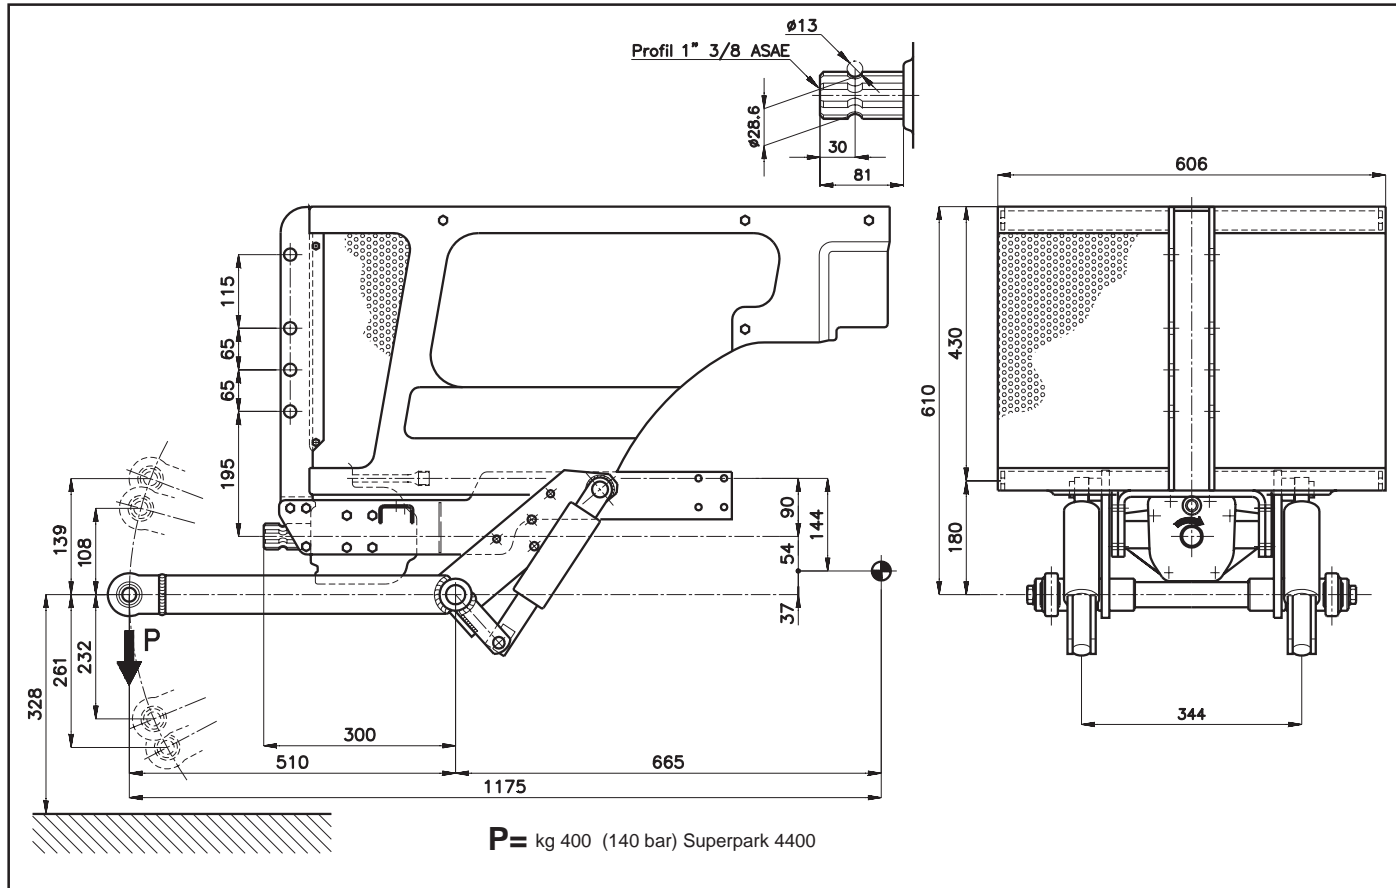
Dimensioner for kobling og flanger ved kraftudtag, med 6.50 - 16 hjul.
